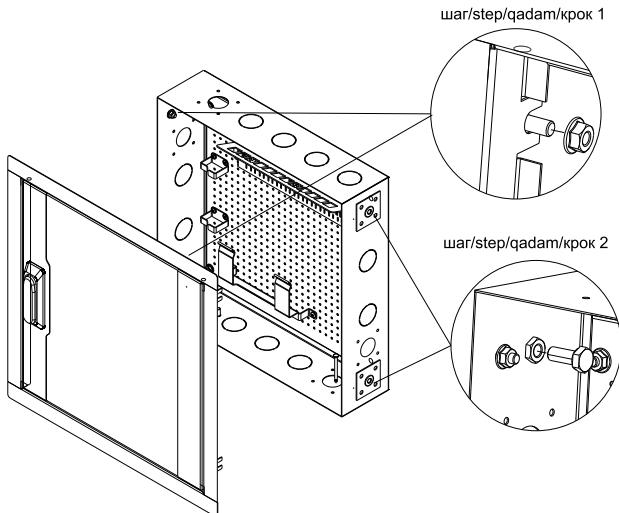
Монтаж корпуса и рамки с дверцей / Figure 3 – Installation of the enclosure and frame with a door / 3-suret – Korpusty jäne esigi bar jiekti montajdau / Рисунок 3 – Монтаж корпусу та рамки з дверцятами
